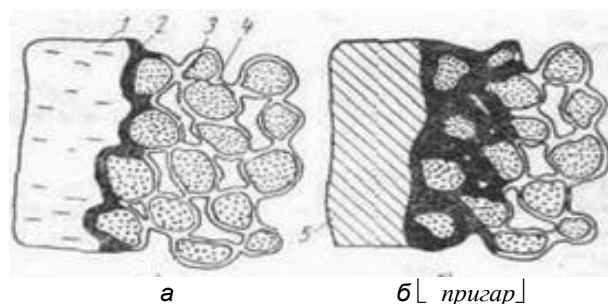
Схема образования пригара на отливках из железо-углеродистых сплавов (чугун/сталь): 1 - жидкий металл; 2 - окислы и силикаты железа; 3 - зерна кварца; 4 - пленка крепителя; а) момент заполнения сплавом полости литейной формы; б) отливка (5 - затвердевший металл), на поверхности которой образовался пригар [1]
